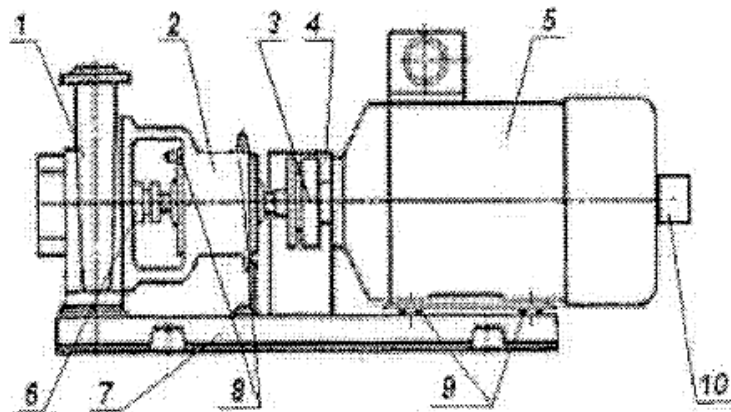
Генераторний блок (турбіна-генератор): 1 - турбіна; 2 - стійка підшипникова; 3 - муфта сполучна; 4 - кожух захисний; 5 - генератор; 6 - ущільнення валу; 7 - платформа; 8 - прес-маслянки підшипників турбіни; 9 - регулювальні шайби; 10 - датчик частоти обертання.
